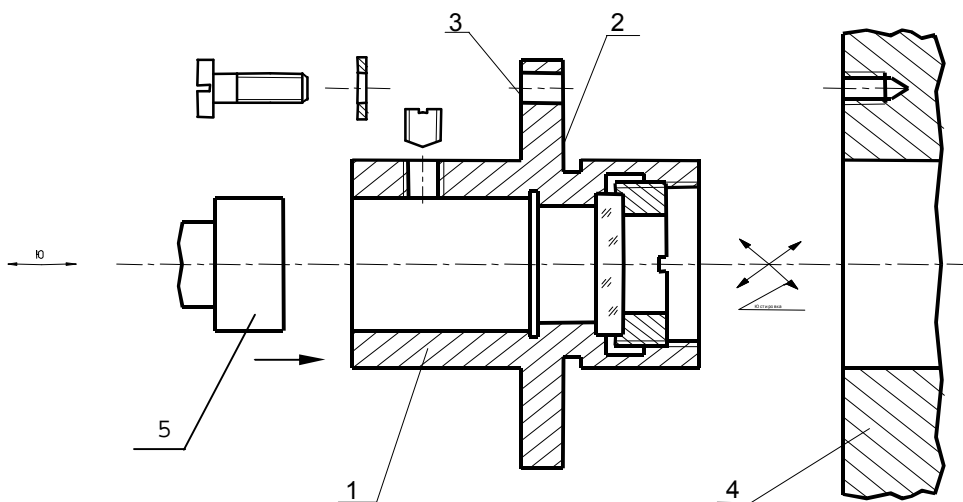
Складний фланець із оптичною деталлю: 1 – циліндричний тубус із оптикою; 2 – фланцева частина; 3 – отвір для кріплення фланця; 4 – корпус; 5 – елемент приладу, установлюваний у тубусі; якщо отвір має діаметр більше діаметра кріплення гвинта, то фланцеву частину можна буде переміщати перпендикулярно оптичній вісі з метою юстування, для цього отвір у корпусі повинен бути більше посадкового діаметра фланця
